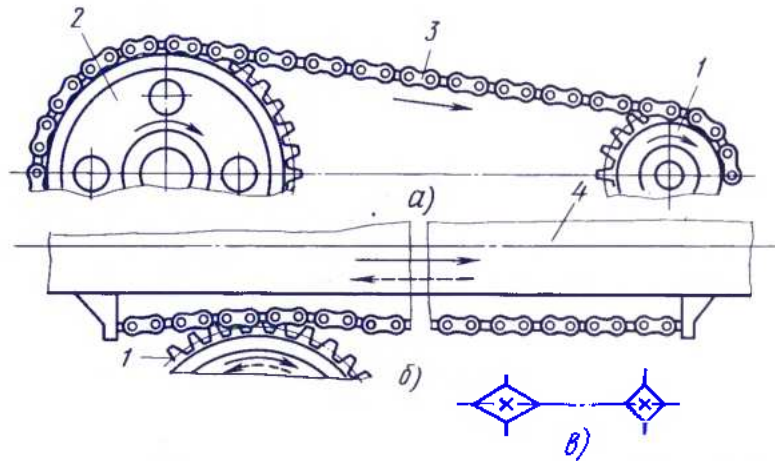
Цепные передачи между двумя параллельными валами (а) для преобразования вращательного движения в поступательное (б) и их обозначение на схеме (в):
